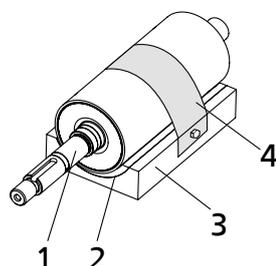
Вспомогательное приспособление для монтажа/демонтажа гильзы подшипника со стороны привода
